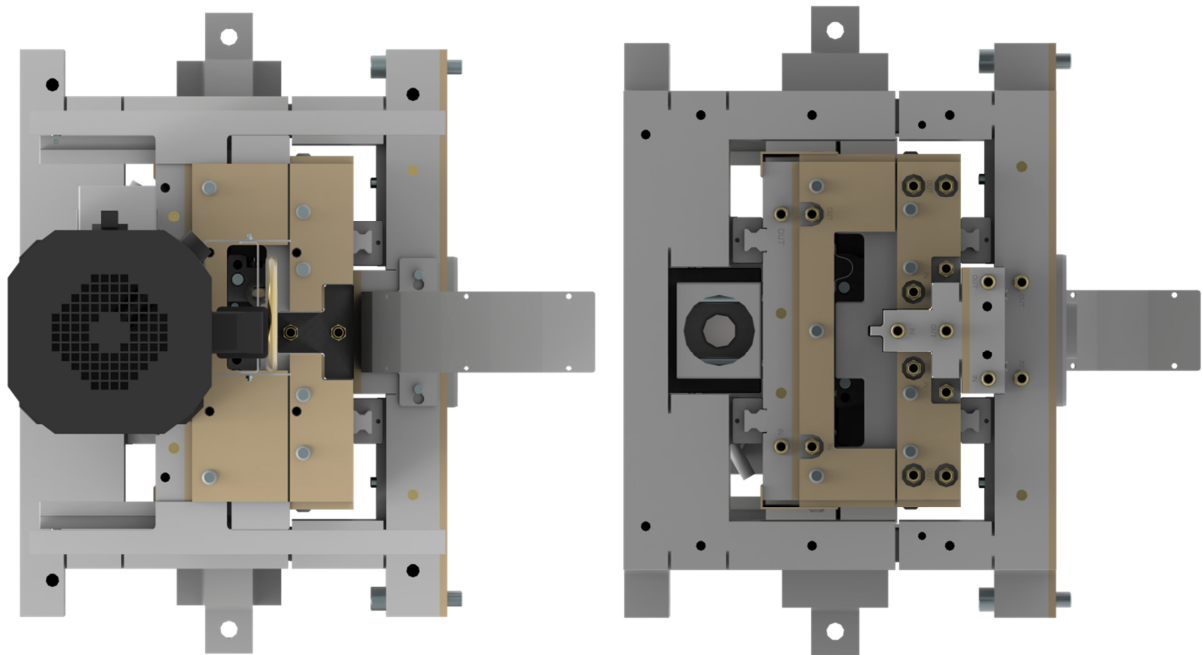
RubExject-Werkzeug in geschlossener Position; Ansicht von oben (links) und unten (rechts) [52].
